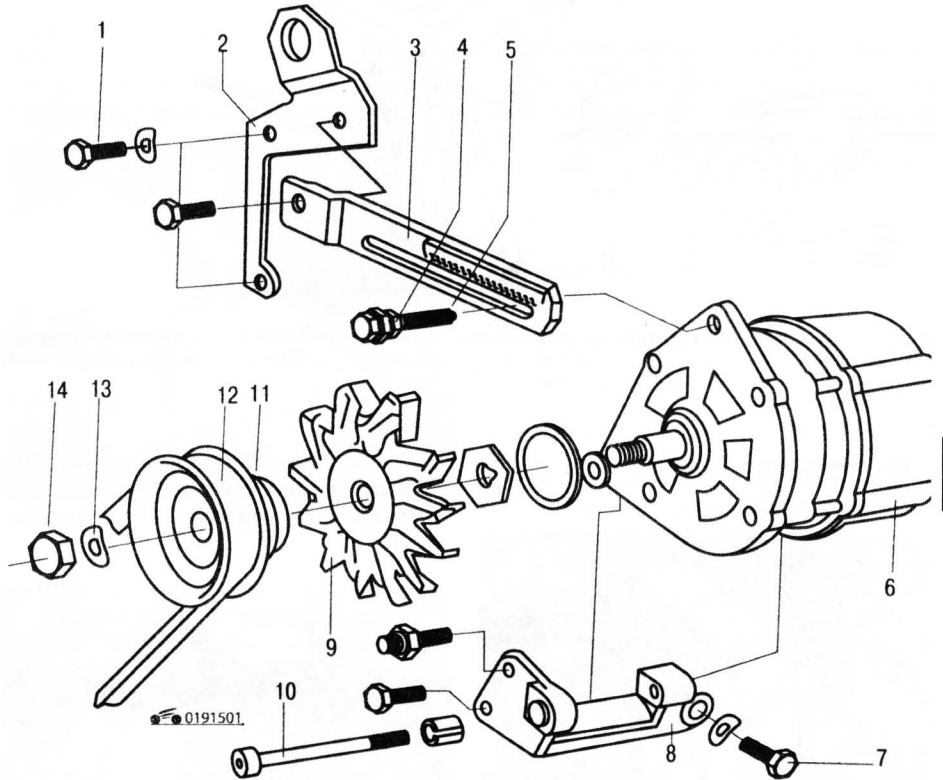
Крепление генератора на автомобилях с двигателями SOHC: 1, 7, 10 – болт; 2 – проушина; 3 – натяжная планка; 4 – регулировочная гайка; 5 – фиксирующий болт; 6 – генератор; 8 – кронштейн; 9 – крыльчатка; 11 – шкив; 12 – приводной ремень; 13 – шайба; 14 – гайка
